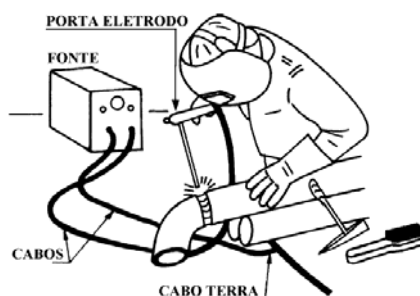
Elementos que compõem o processo de soldagem com eletrodo revestido.
